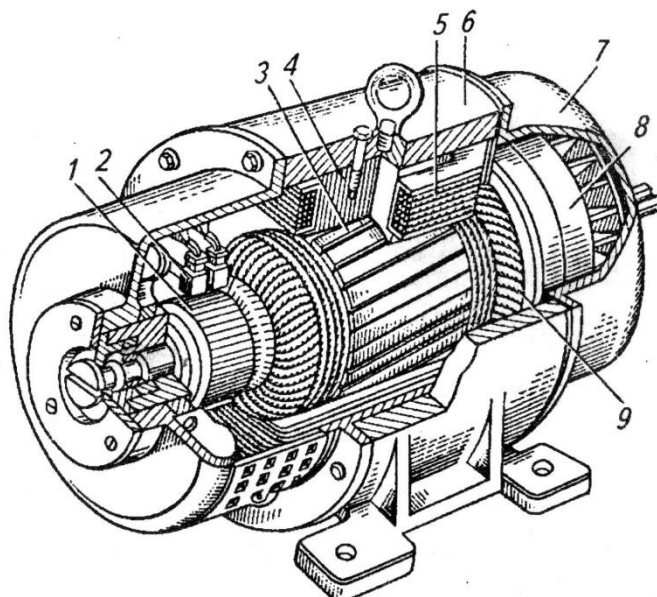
Устройство машины постоянного тока: 1 — коллектор; 2 — щетки; 3 — сердечник якоря; 4 — главный полюс; 5 — катушки обмотки возбуждения; 6 — корпус (станина); 7 — подшипниковый щит; 8 — вентилятор; 9 — обмотка якоря
